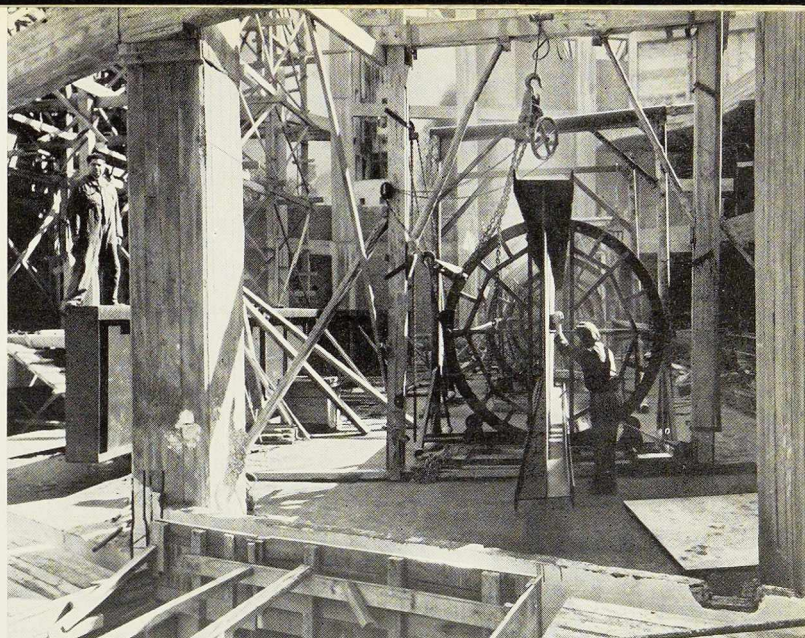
Une des poutres placée sur le positionneur, permettant d'éviter les soudures au plafond.
